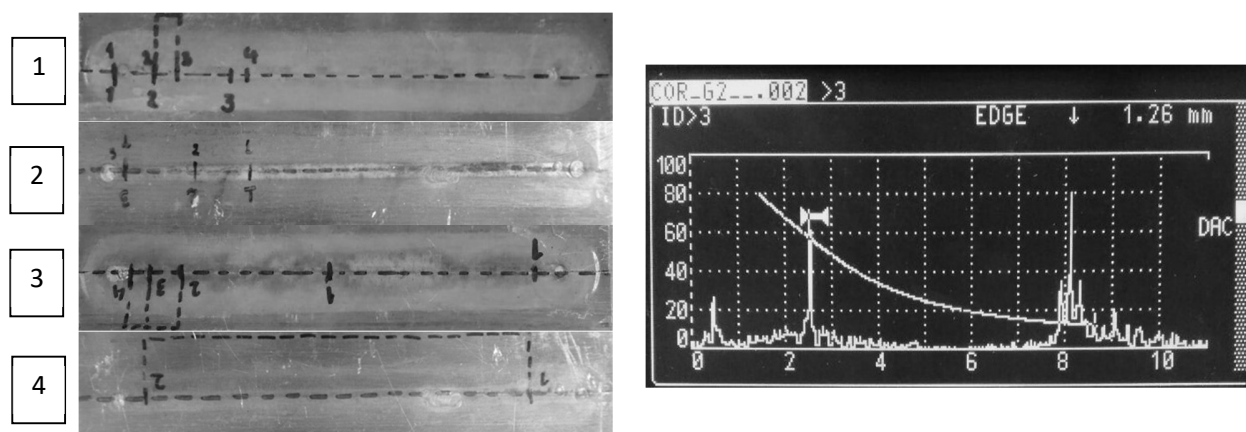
Indicaciones de UT sobre cordones de soldadura obtenidos mediante FSW.
